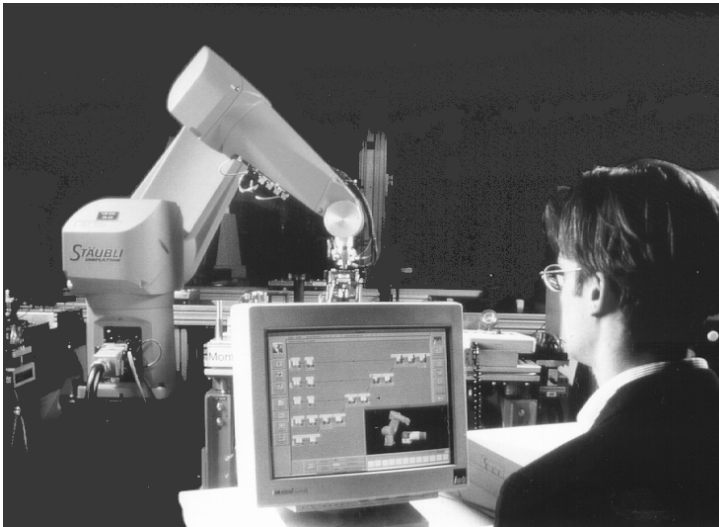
Steuerung der realen Dosenöffnermontage mit CosMonAut
